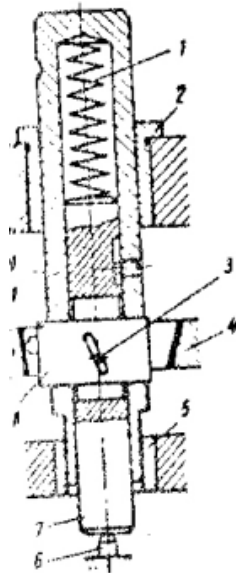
Приспособление для расточки конусного отверстия на вертикально-сверлильном станке.
